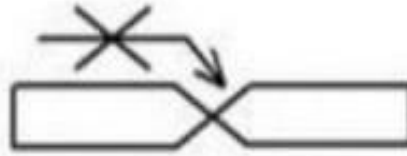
Kumpuh V tunggal *Single V butt weld* (Aji, 2019)
